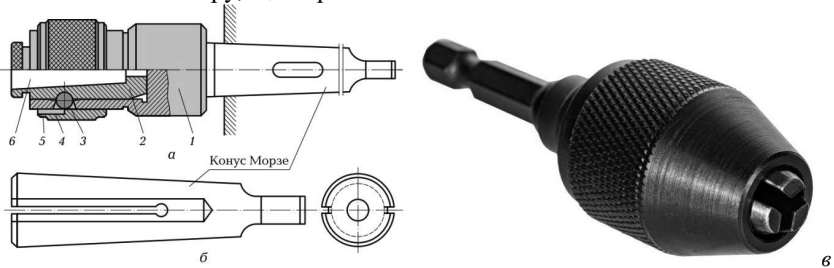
Швидкозмінний патрон свердильний: а – конструкція: 1 – корпус; 2 – змінна втулка; 3 – кулька; 4 – кільце; 5 – виточення; 6 – конічний отвір; б – змінна втулка; в – зовнішній вид
